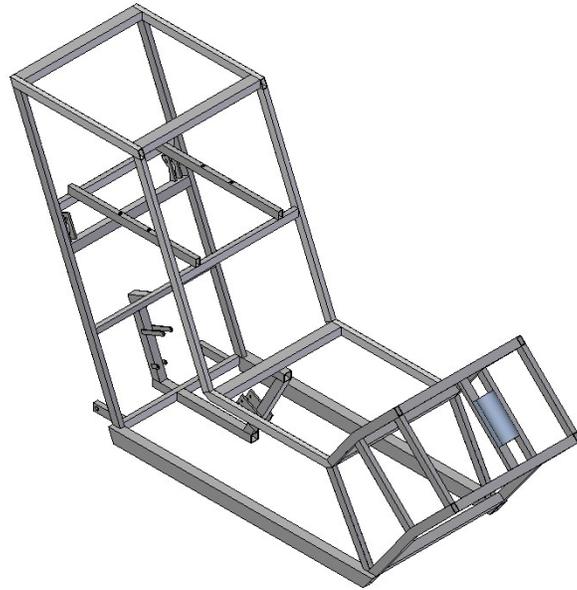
Chasis Diseñado para la Moto en Construcción.
